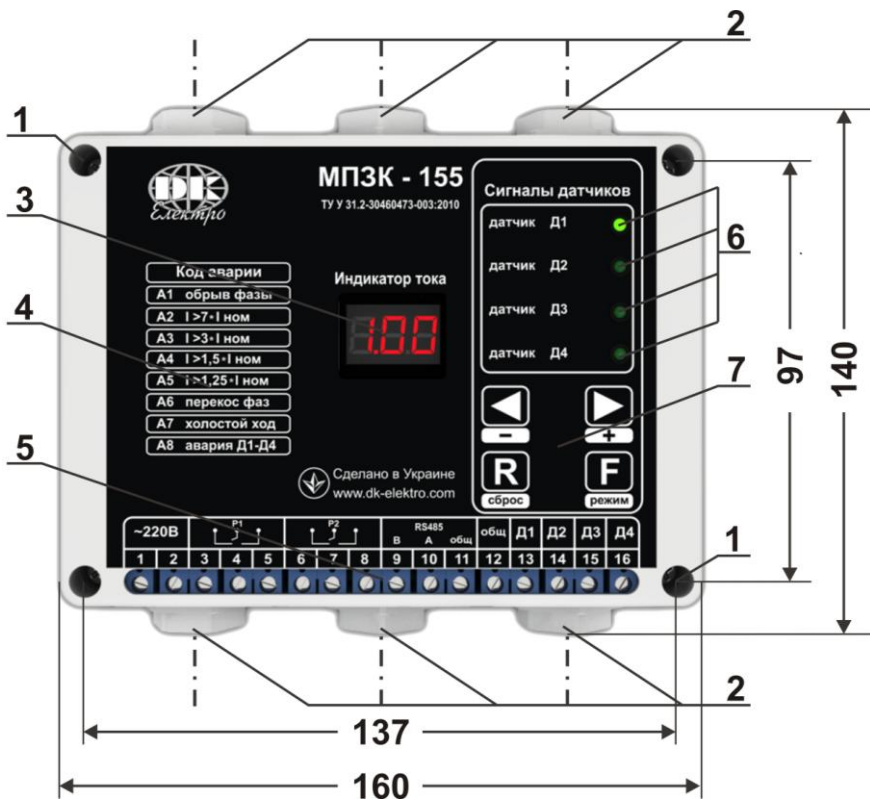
Внешний вид. Габаритные и установочные размеры прибора.
